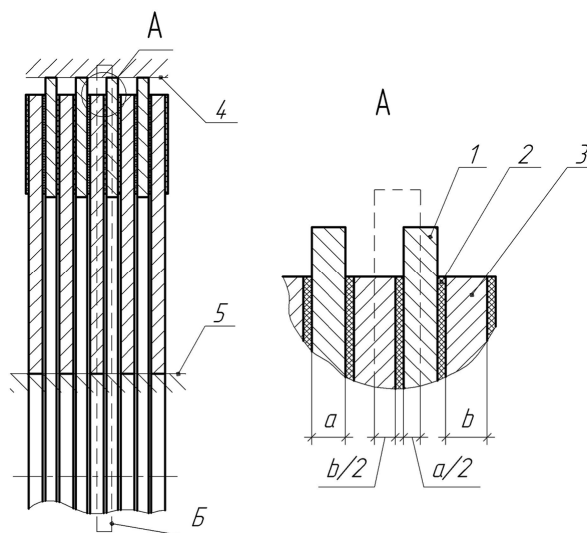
Схема расположения тормозных и промежуточных дисков в ММОТ: 1 — промежуточный диск; 2 — фрикционный материал; 3 — металлическая основа тормозного диска; 4 — корпус тормоза; 5 — вал тормоза
